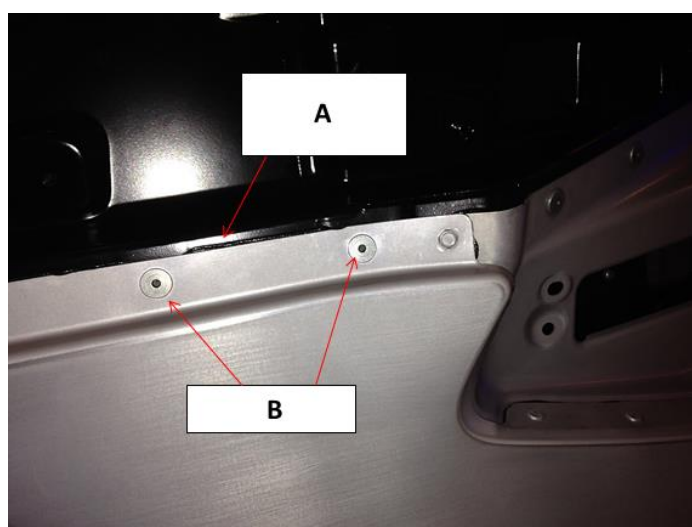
A. Adhesivo estructural, B. Remaches ciegos. Fuente: TWI
